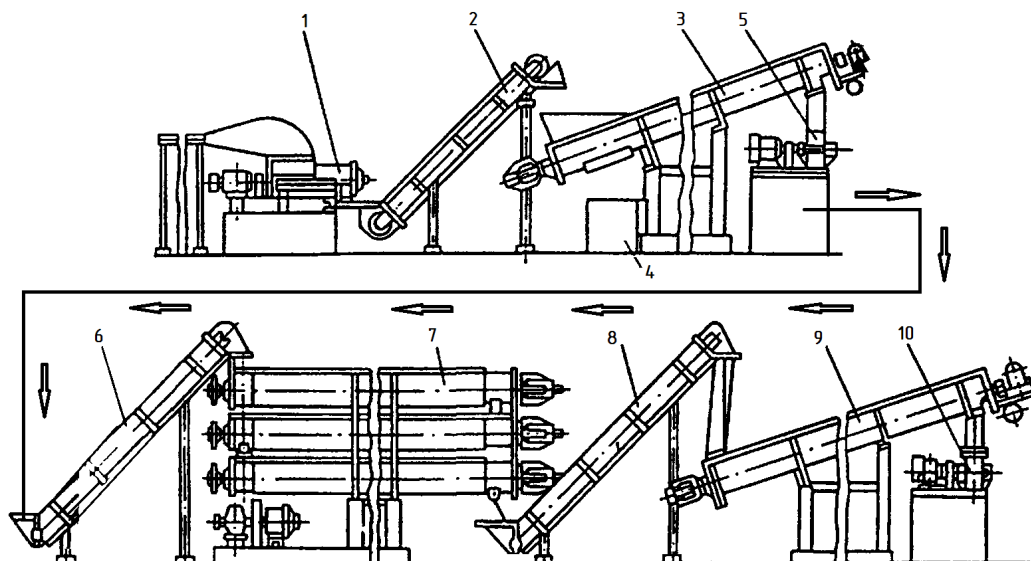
Лінія К7-ФКЕ: 1 – подрібнювач; 2 – елеватор; 3 – збезводнювача; 4 – жироловки; 5, 10 – дробарки; 6, 8 – елеватори обігріваються; 7 – сушильний агрегат; 9 – охолоджувач..
